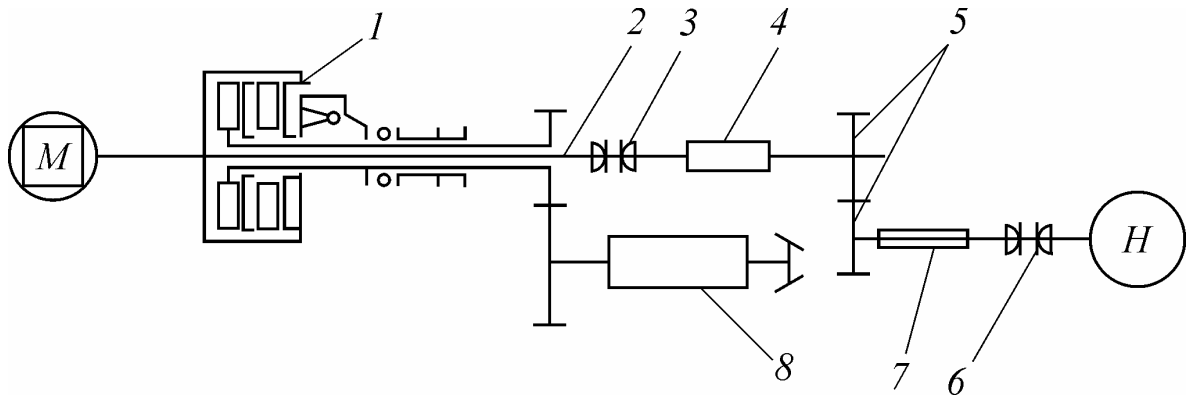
Кинематическая схема независимого ВОМ: 1 – муфта сцепления; 2, 7 – валы; 3, 6 – карданная передача; 4 – редуктор ВОМ; 5 – зубчатая пара редуктора ВОМ; 8 – коробка передач
